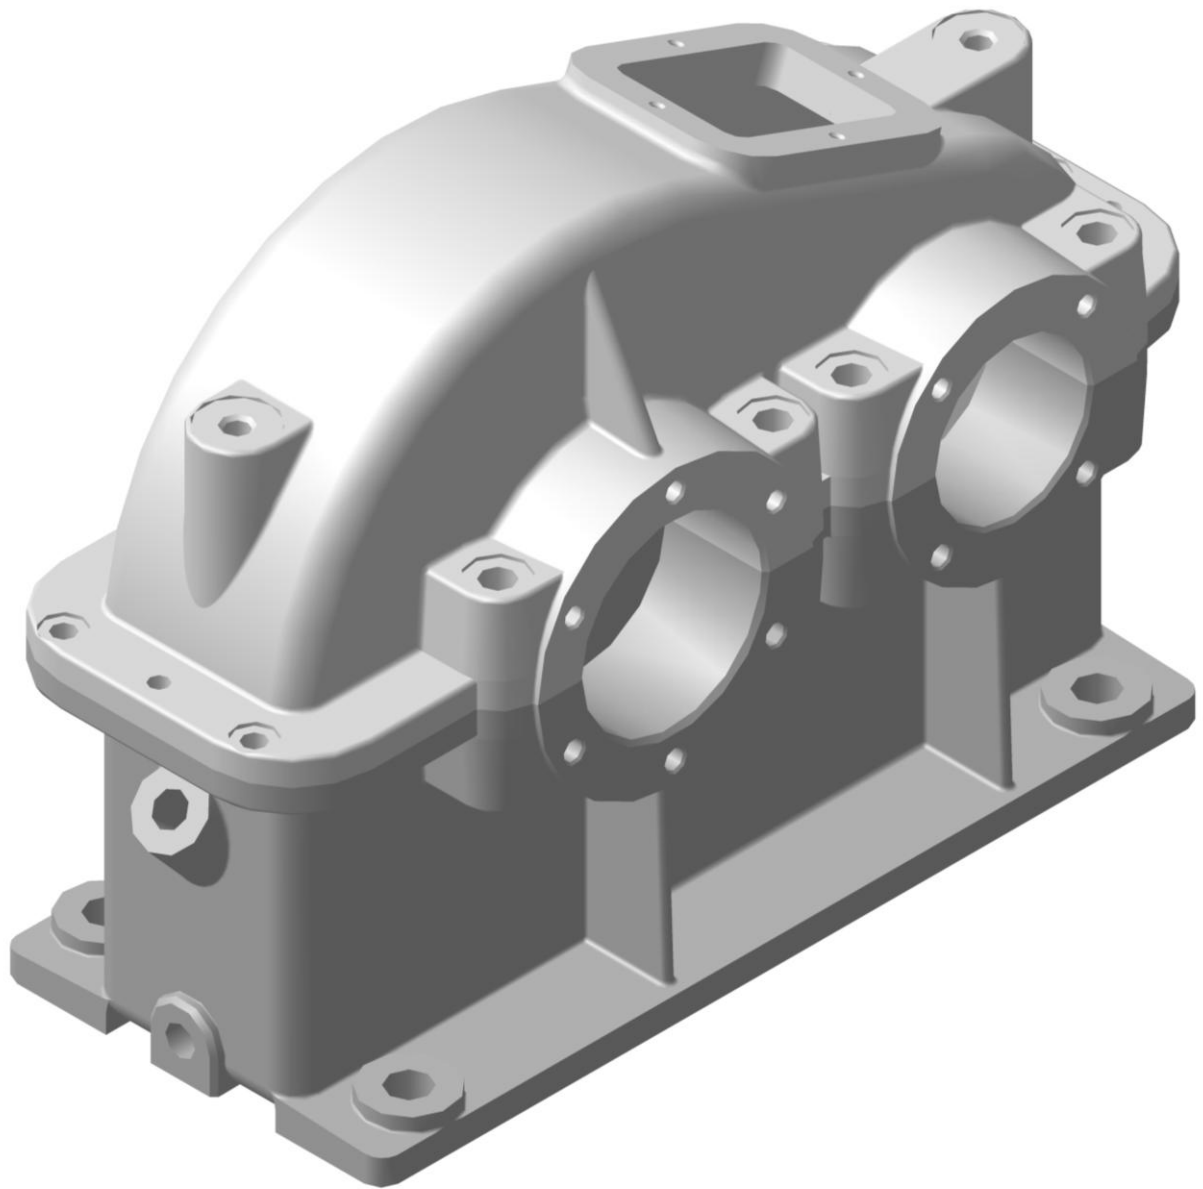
(лист 3, листов 3) Конструкции корпусных деталей цилиндрических редукторов с наружным расположением подшипниковых бобышек
